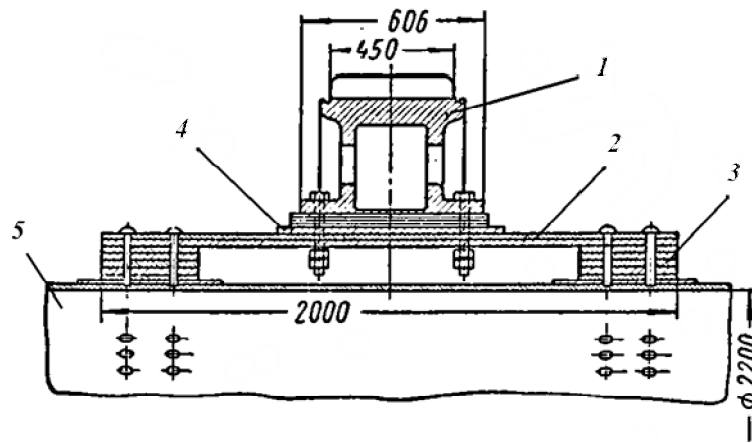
Крепление зубчатого венца к барабану при помощи пружин, расположенных вдоль образующей корпуса:
